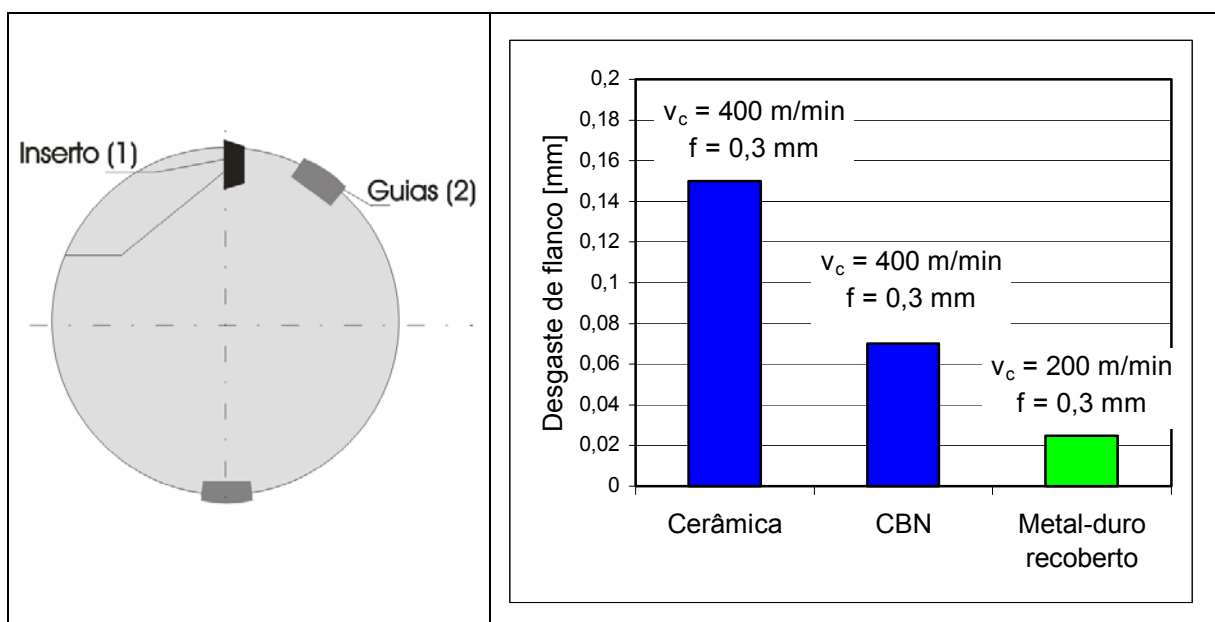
Desgaste de flanco após 64 cilindros usinados por uma ferramenta com um único inserto (Kress, 2000).
